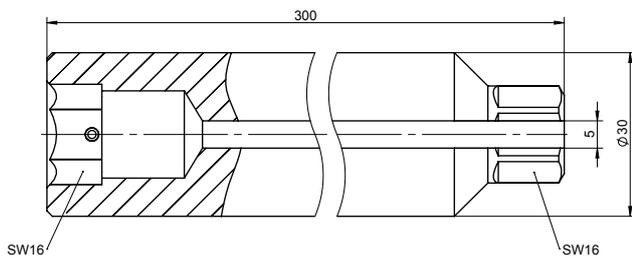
Montageschlüssel geschlitzt, Typ 1251A21A
